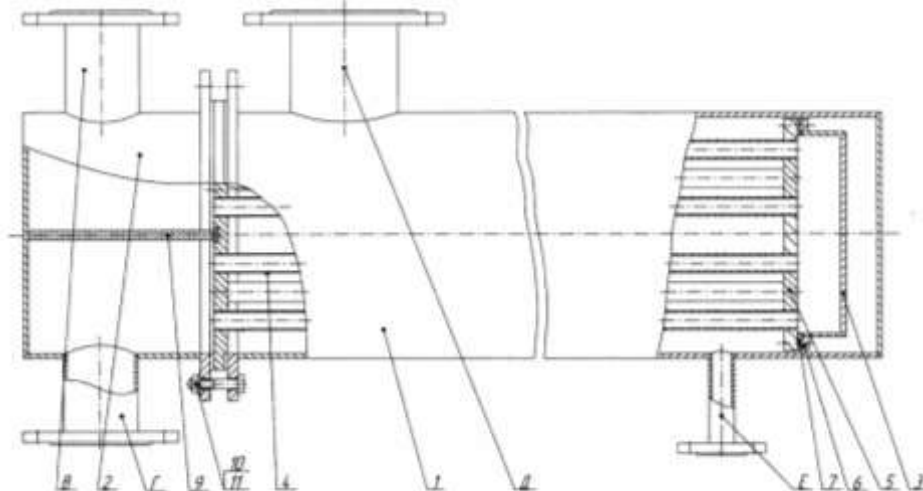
Теплообмінник з плаваючою головою і роз'ємним опорним кільцем: 1 – кожух; 2 - продуктова камера; 3 - плаваюча головка; 4 – трубка; 5- трубна дошка; 7 – прокладка; 9 – перегородка; 10,11-болтове з'єднання
